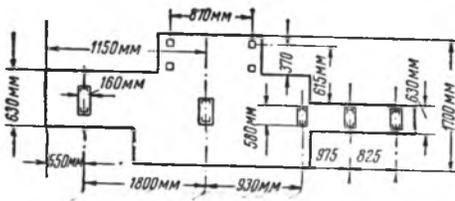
Установочный чертеж станка модели ЦДТ-5.
